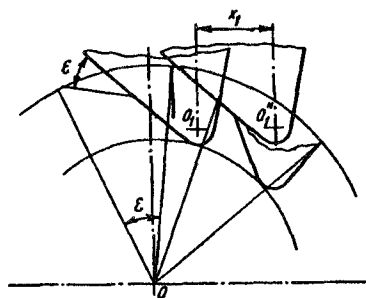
Схема настройки для фрезерования спинки зуба храпового колеса
